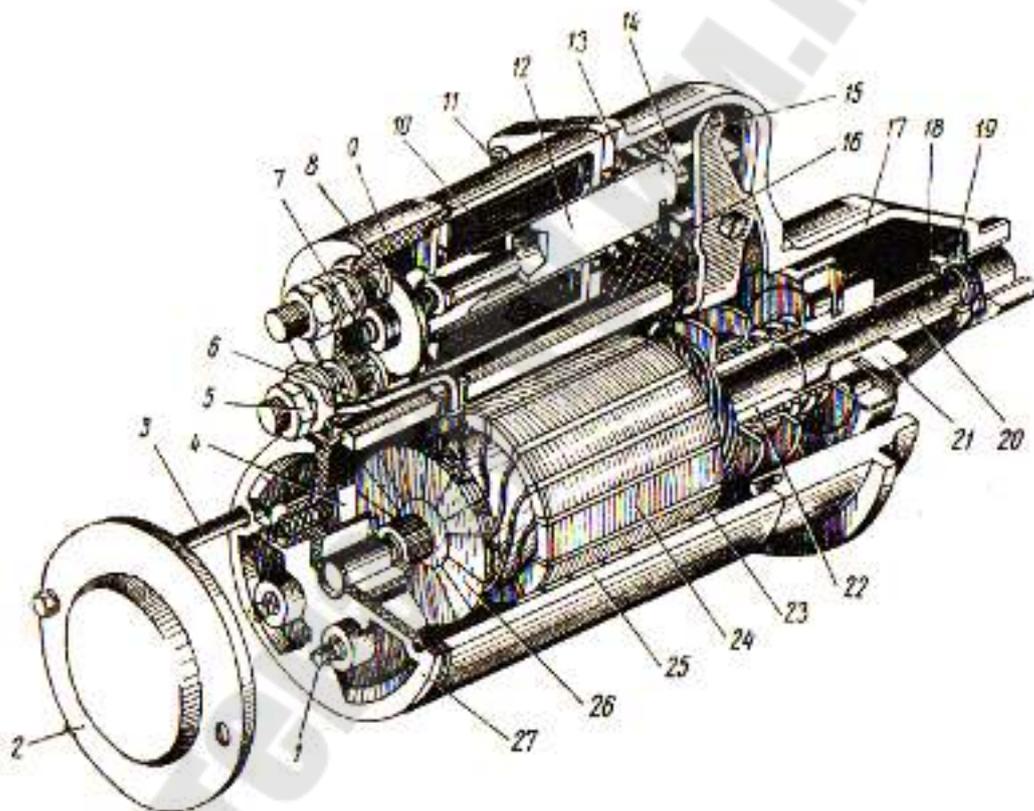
Стартер 3212.3708: 1 – пружина щеткодержателя; 2 – задняя крышка; 3 – шпилька; 4 – щетка; 5, 7 – болты тягового реле; 6 – вывод обмотки возбуждения; 8 – крышка тягового реле; 9 – контактный диск; 10 – обмотки тягового реле; 11 – болты крепления тягового реле; 12 – якорь тягового реле; 13 – возвратная пружина; 14 – петля якоря тягового реле; 15 – рычаг; 16 – резиновая прокладка; 17 – передняя крышка; 18 – стопорное кольцо; 19 – пружинный фиксатор; 20 – вал якоря; 21 – шестерня привода; 22 – привод; 23 – обмотка якоря; 24 – сердечник якоря; 25 – корпус статора; 26 – коллектор; 27 – щеткодержатель
